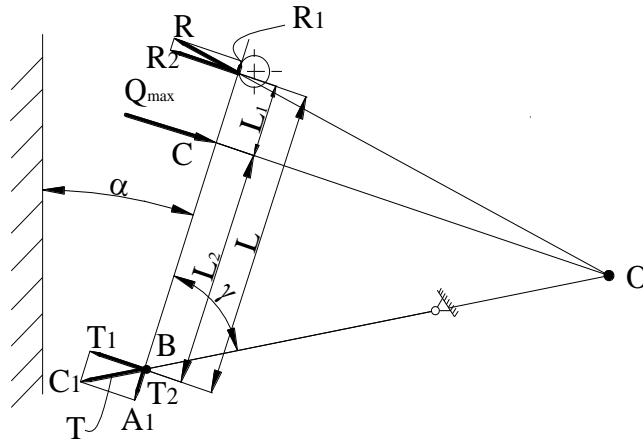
Розрахункова схема для визначення зусиль у деталях щокової дробарки зі складним коливанням щоки
